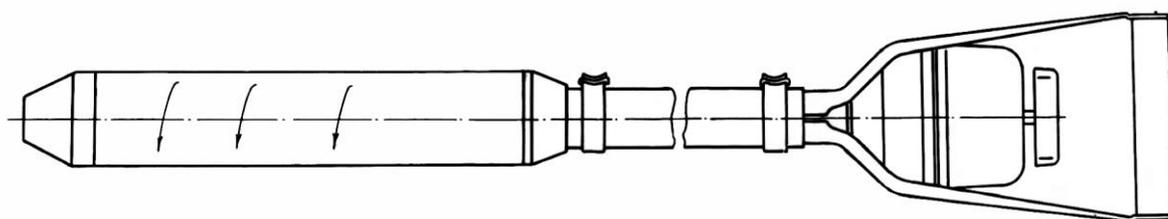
Схема установления направления вращения вала ротора вибраторов ИВ-78, ИВ-102А.
